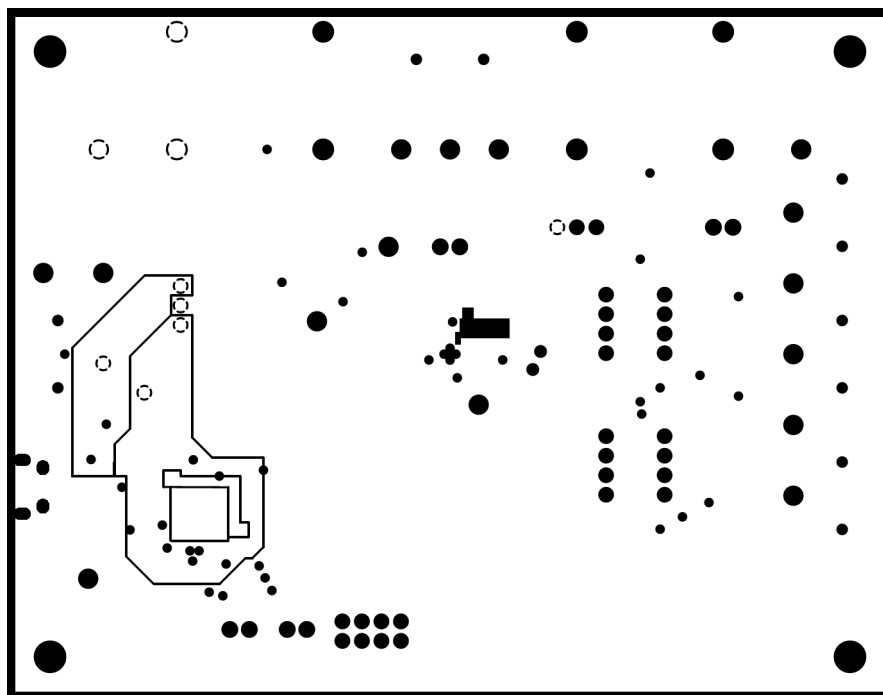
DAC8831EVM PCB 中层 2 布局 (电源平面)
